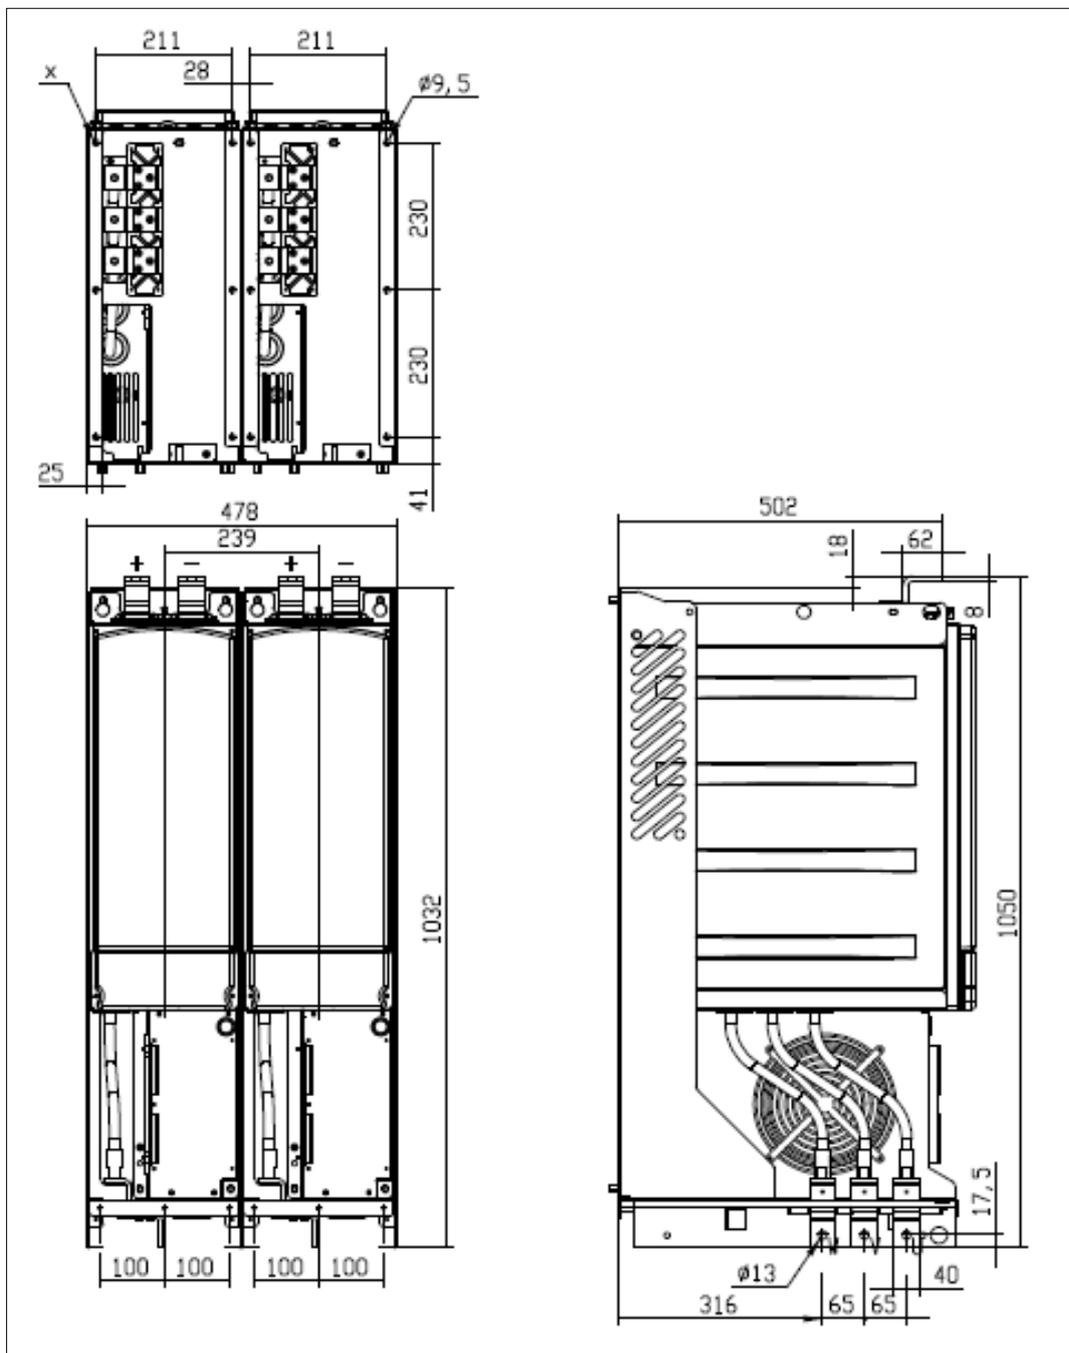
Dimensiones del inversor Vacon NXI, vista frontal del FI12
